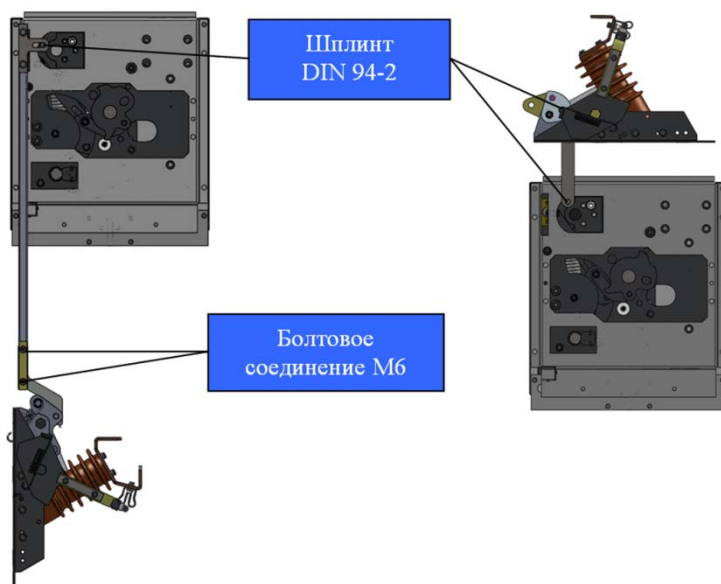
г. Крепление тяги дополнительного заземляющего разъединителя.
